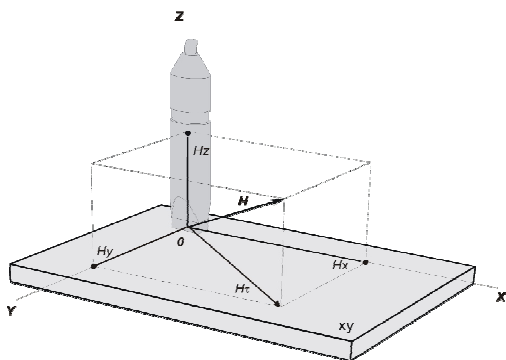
Положение ФП на поверхности контролируемой детали:
